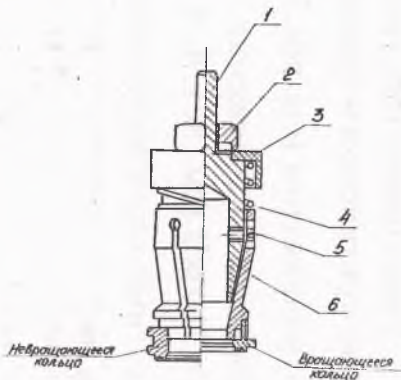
Приспособление для снятия фасок: 1 – сердечник; 2 – гайка; 3 – упор; 4 – пружина; 5 – стопорный винт; 6 – цанга.
